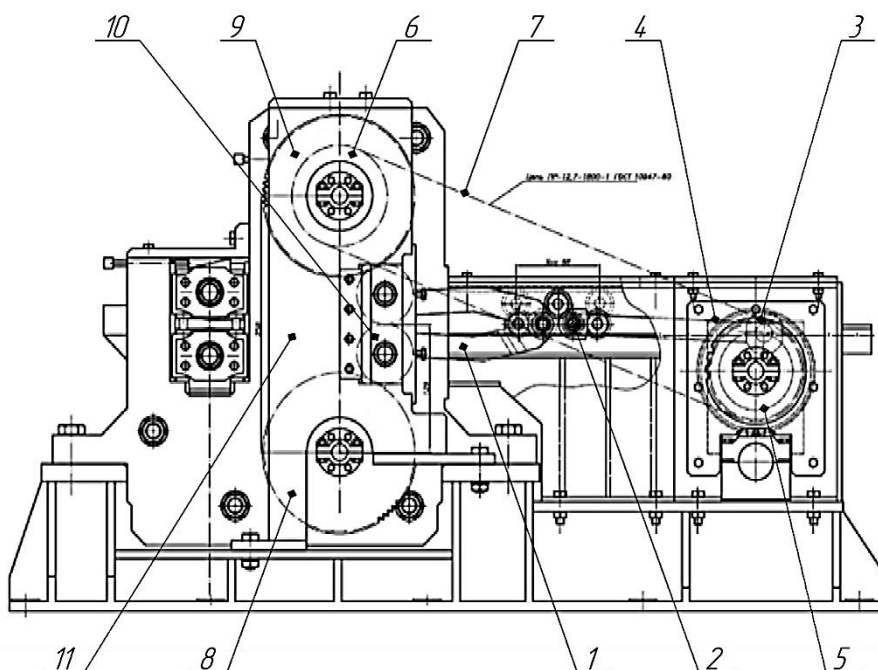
Конструктивное изображение маятникового стана с цепным приводом
